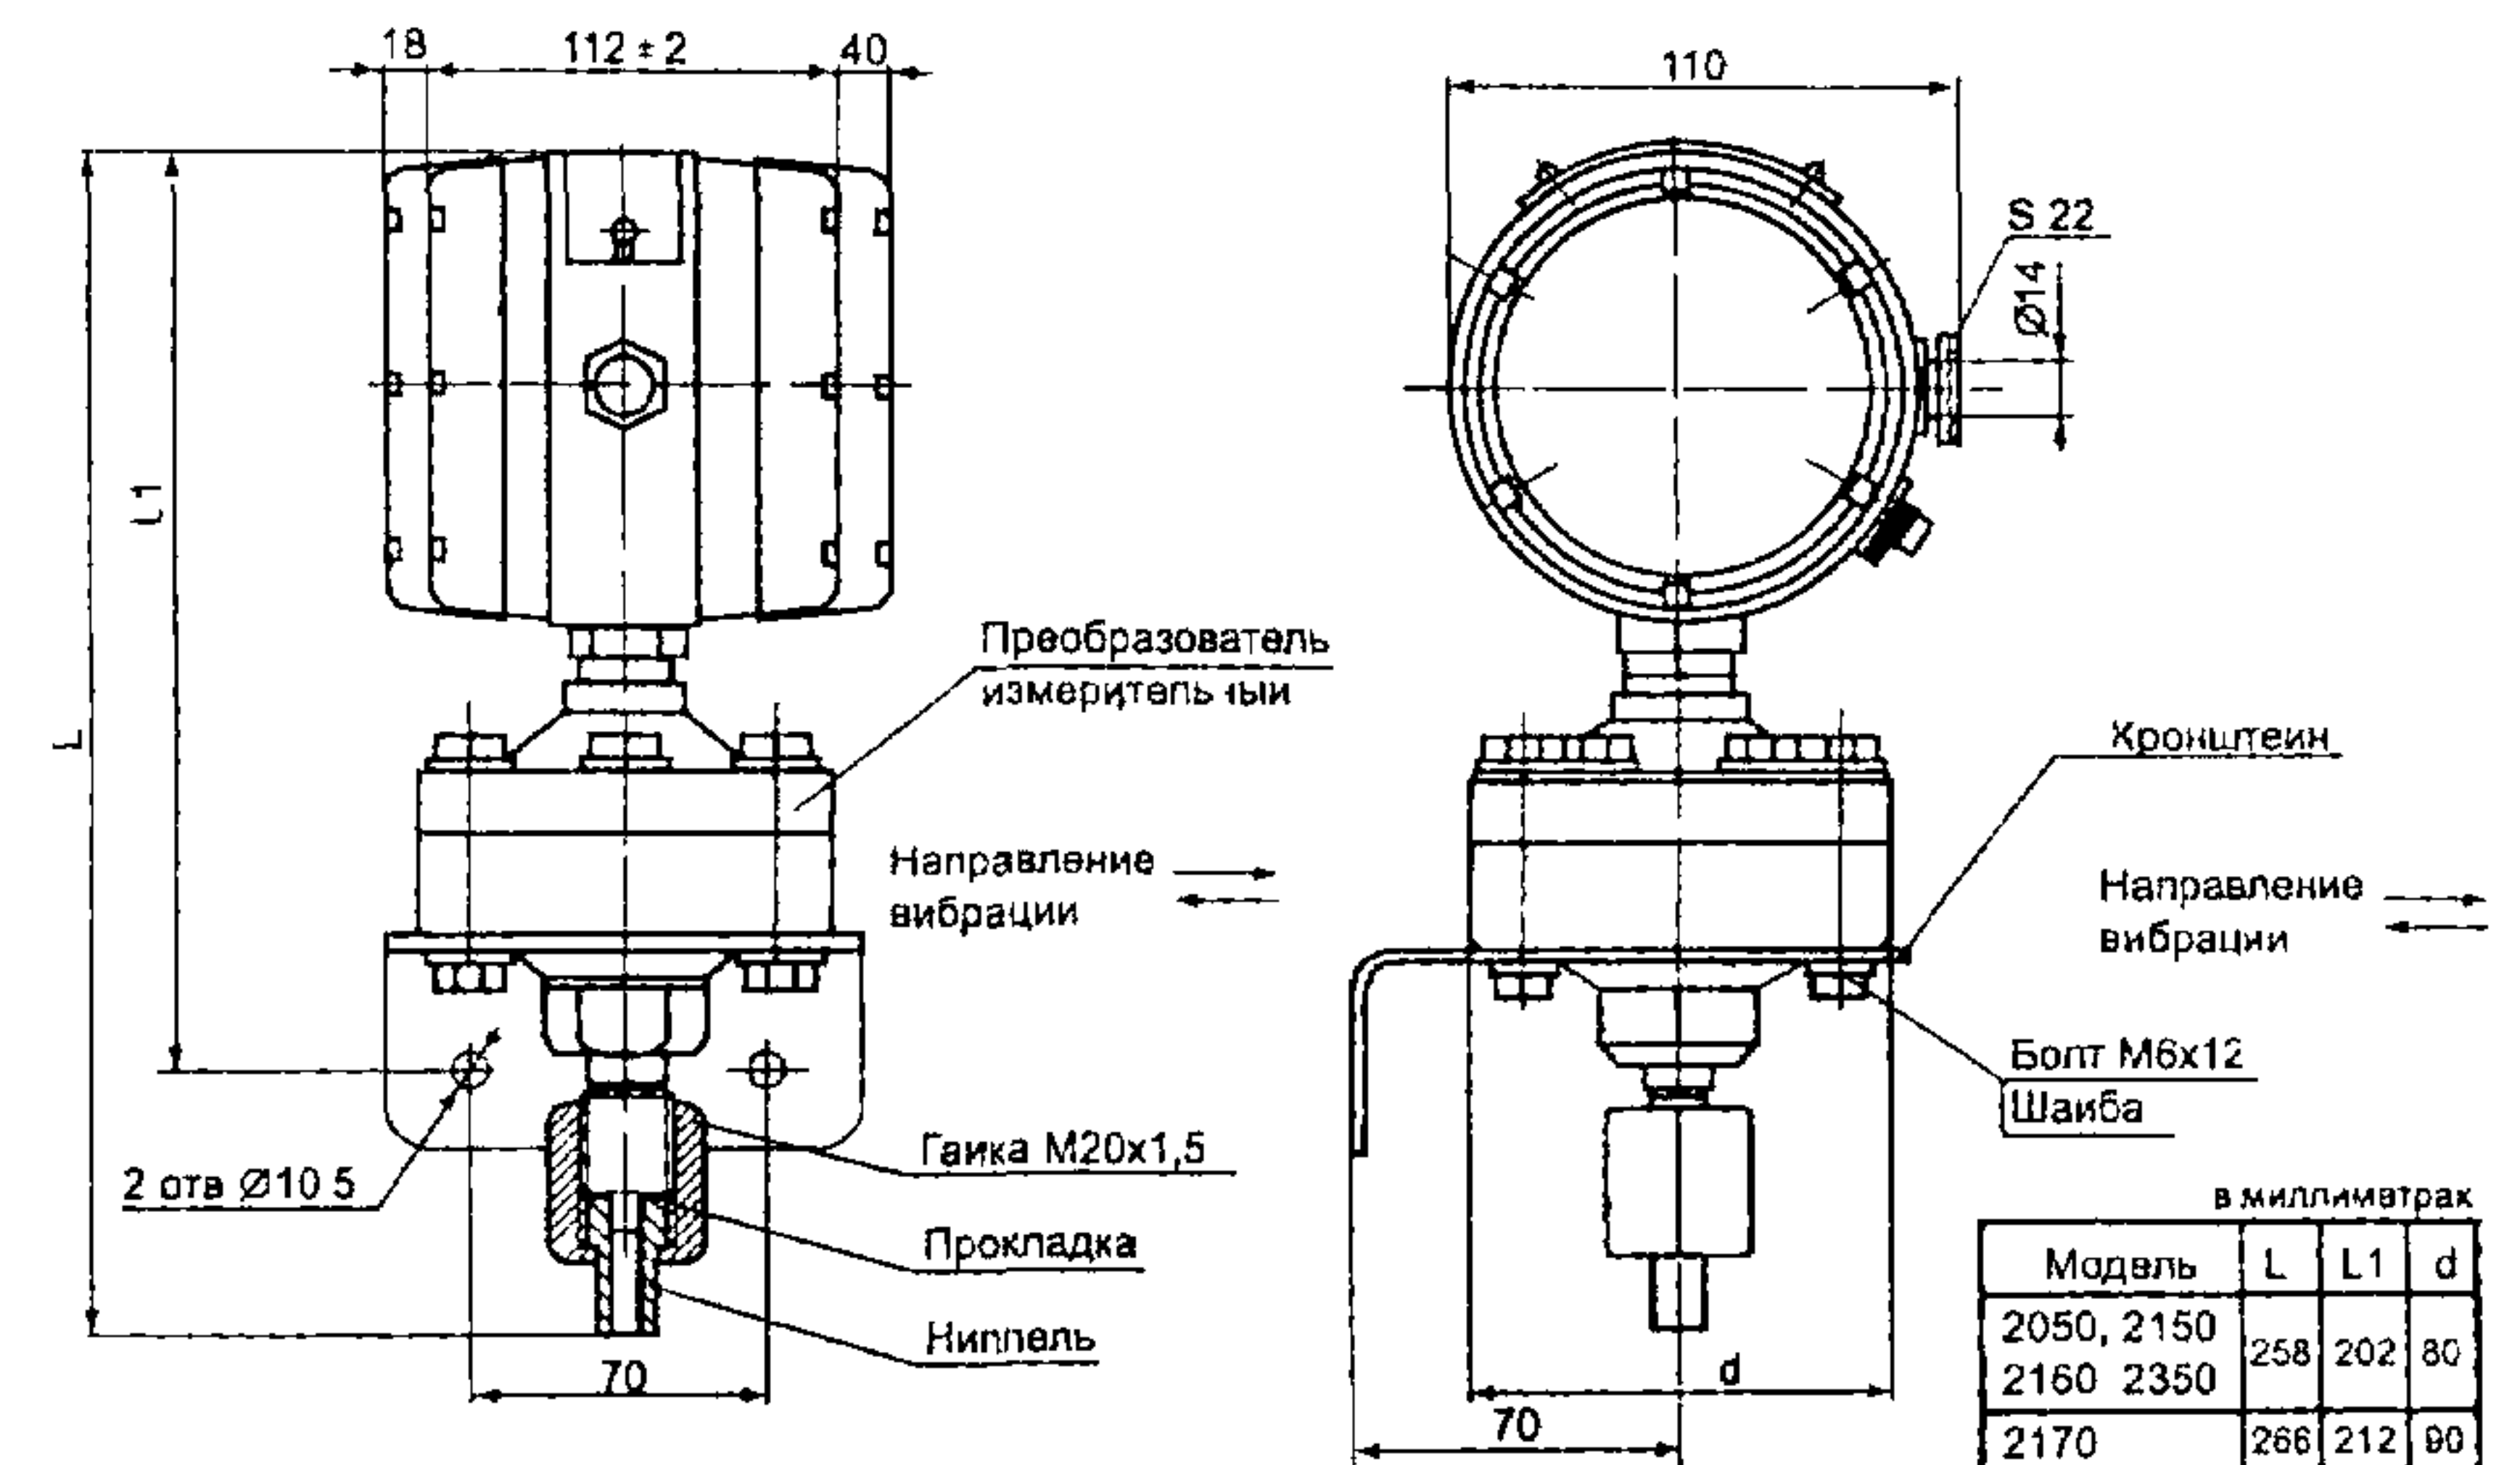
Установочные и присоединительные размеры преобразователей Сафир-22Р моделей 2050, 2150, 2160, 2170, 2350
